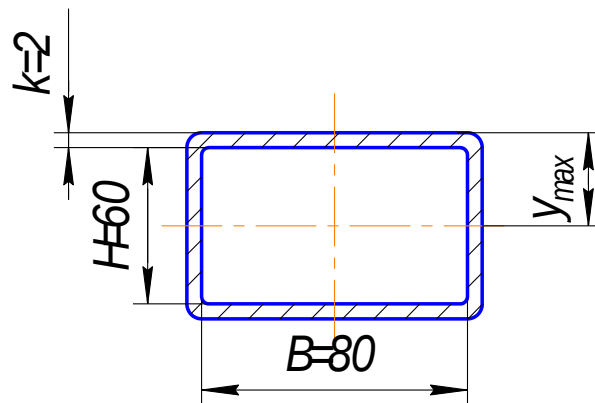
Розрахунковий переріз зварного з'єднання
